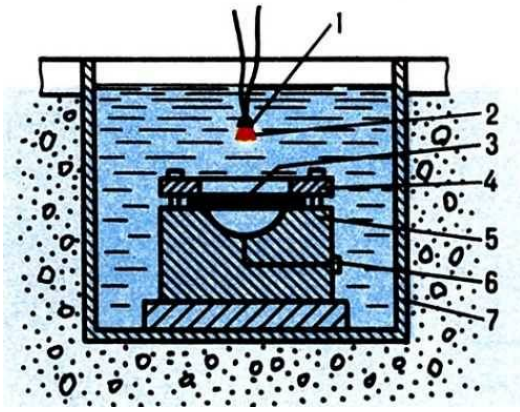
Штампування вибухом: 1 – детонатор; 2 – вибухова речовина; 3 – заготівка; 4 – притискна планка; 5 – матриця; 6 – штуцер для приєднання вакуум-насоса; 7 – резервуар з водою
